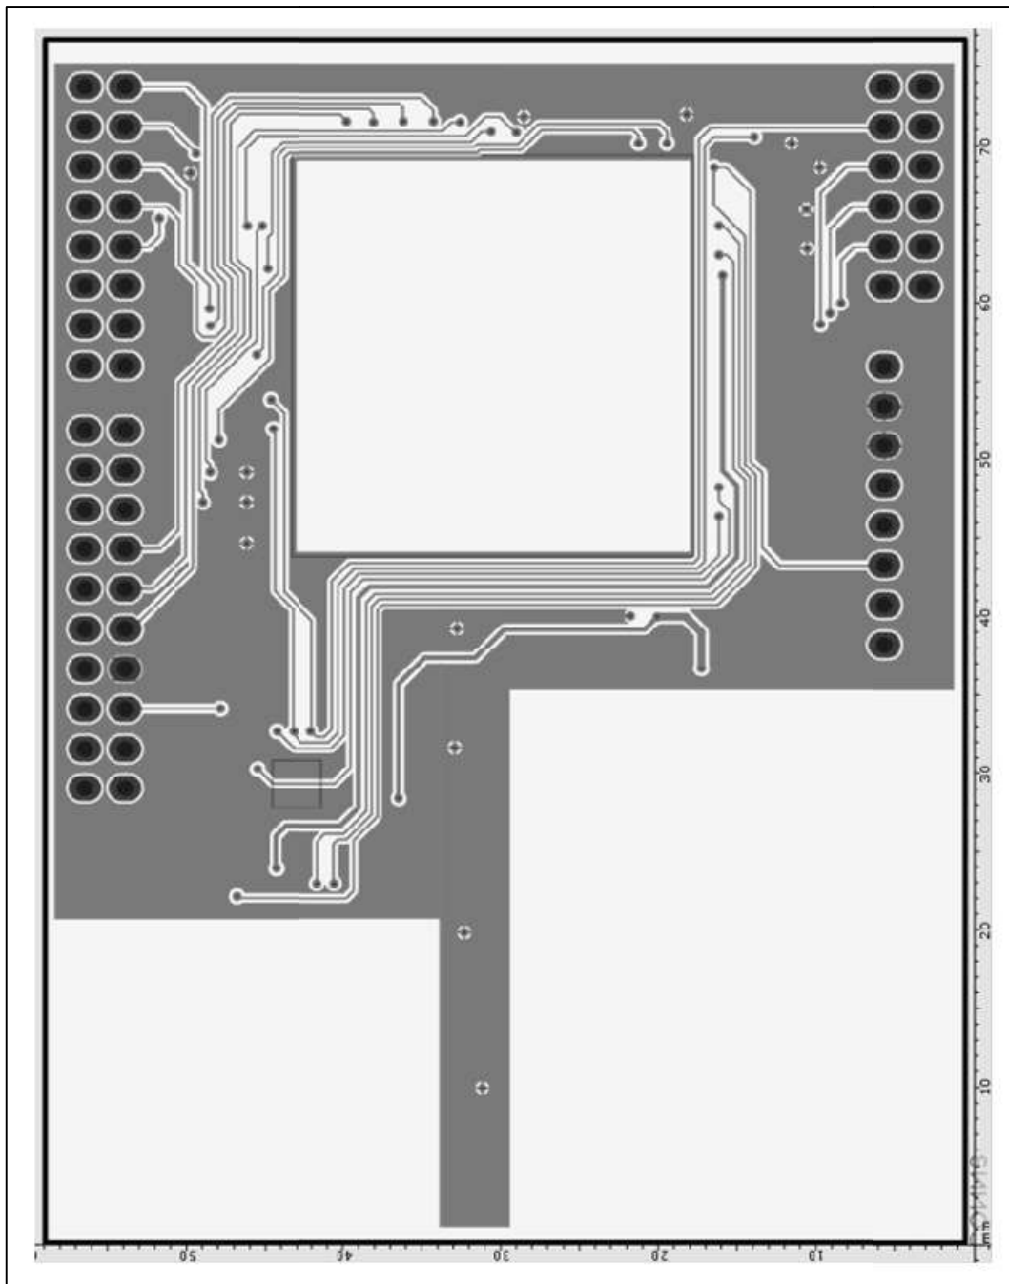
Bloque externo unificador, vista PCB: cara BOTTOM
